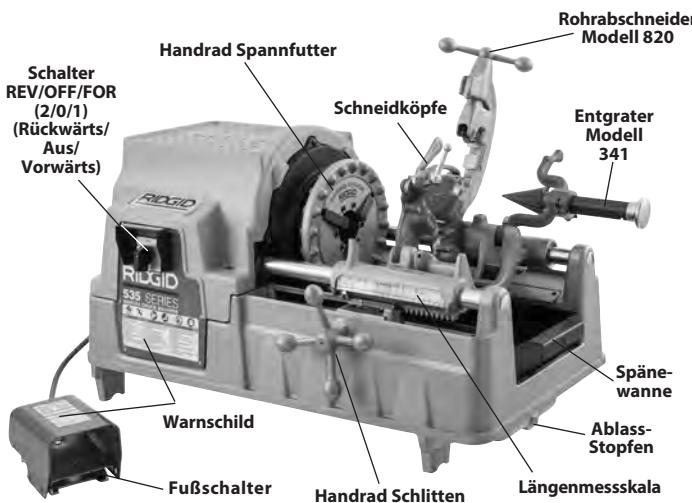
A – Gewindeschneidmaschine 535 mit Handspannfutter
